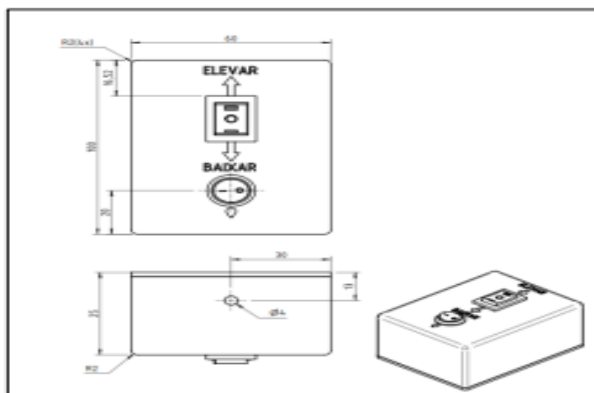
Case para montagem de componentes eletrônicos Fonte: Autor
